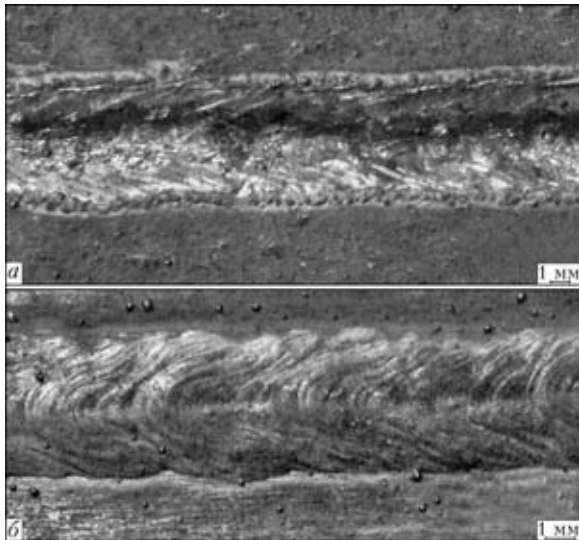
Вид поверхности стыкового соединения легированной стали после лазерной сварки без (а) и с расплавлением (б) присадочной проволоки
